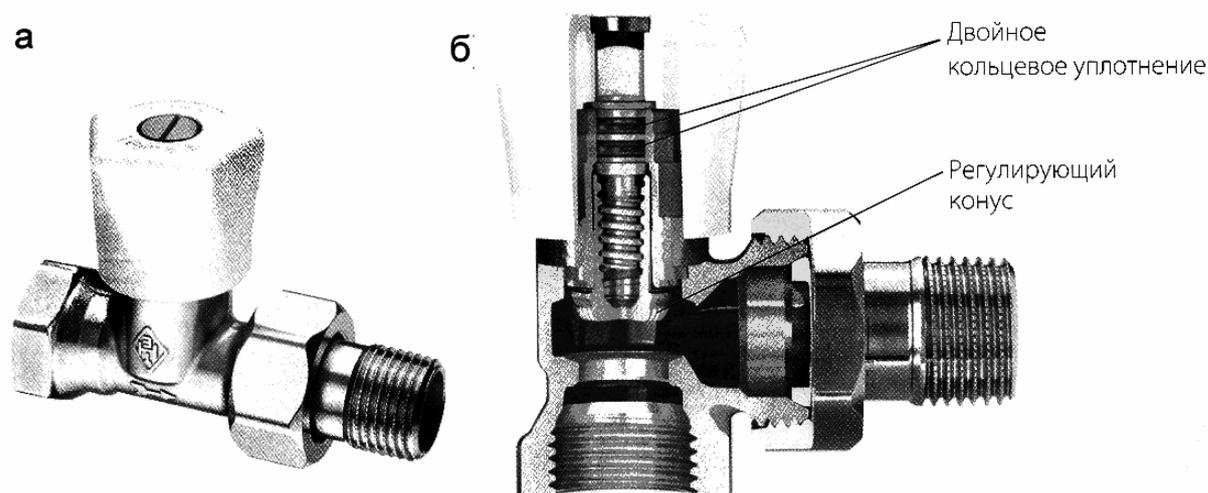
Общий вид и конструкция регулировочного вентиля:
